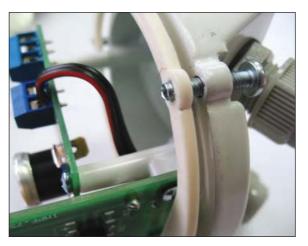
Соединение задней крышки с цилиндрическим корпусом для гермобокса серии ТГБ-5
